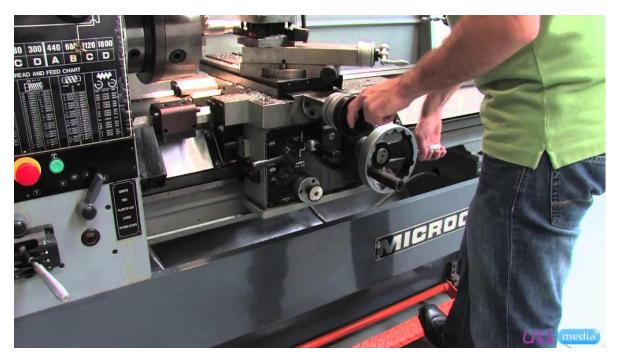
Fabricación en torno paralelo. 2014 Fuente. https://www.youtube.com/watch?v=JtH8Qd17FW0
